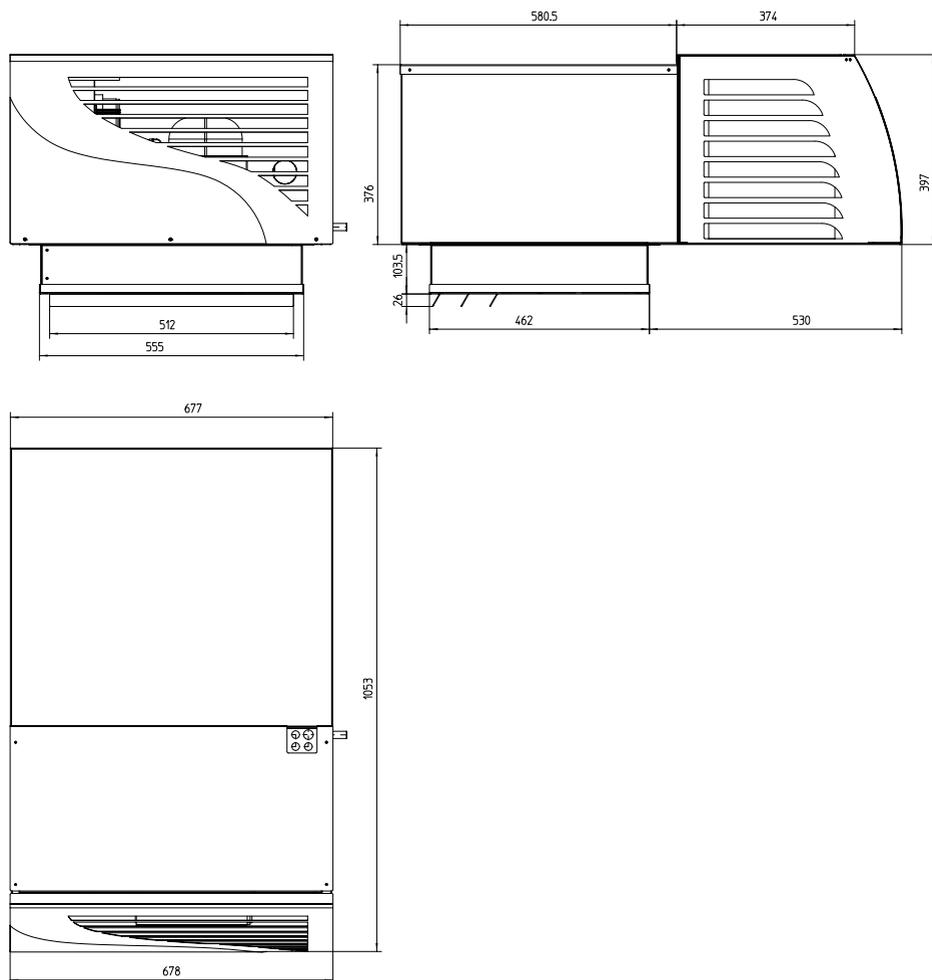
Dimensiones of 7 TN1, 5 TL1
